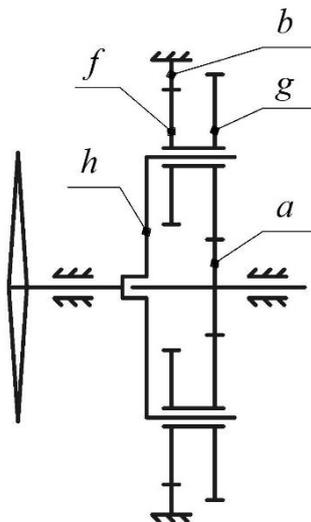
Кинематическая схема планетарной передачи с двухвенцовыми сателлитами
